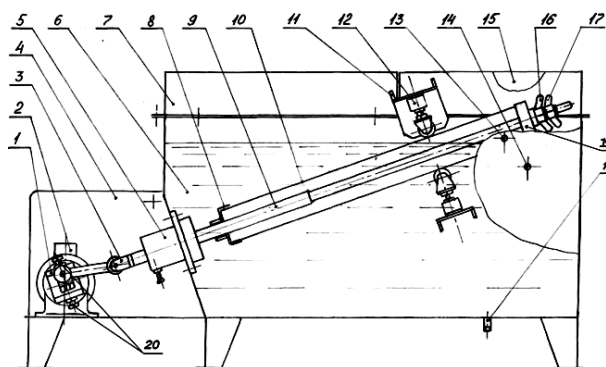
Схема установки для кавитационной мойки трубчатых деталей: 1 – механизм привода; 2 – электродвигатель; 3 – регулируемая вилка; 4 – кожух; 5 – втулка; 6 – ёмкость; 7 – крышка несъёмная; 8 – нижний фланец крепления трубы; 9 – шток; 10 – обрабатываемое изделие; 11 – балка; 12 – роликовая опора; 13 – штуцер заливной; 14 – штуцер контроля
